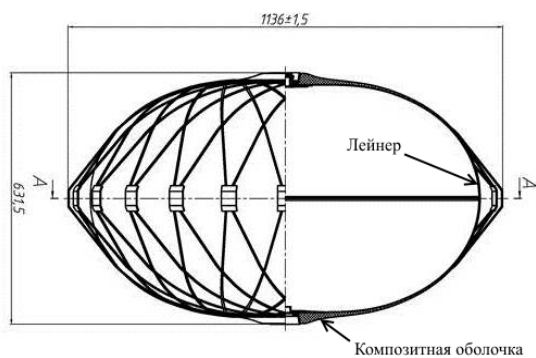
Конструктивная схема и основные размеры металлокомпозитного бака высокого давления
